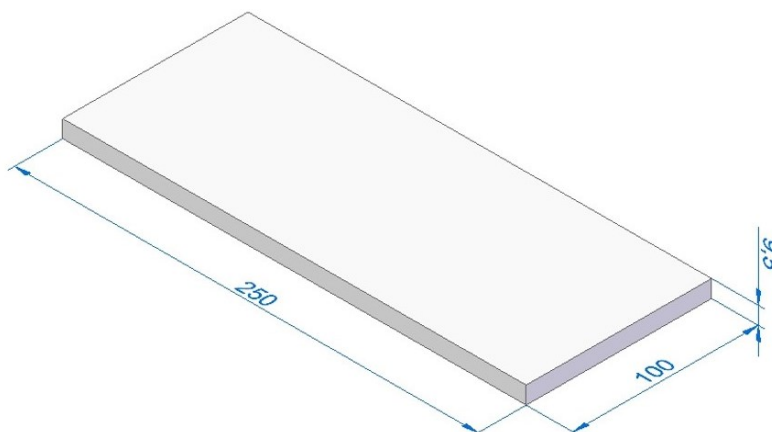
Dimensões dos corpos de prova, em milímetro.
